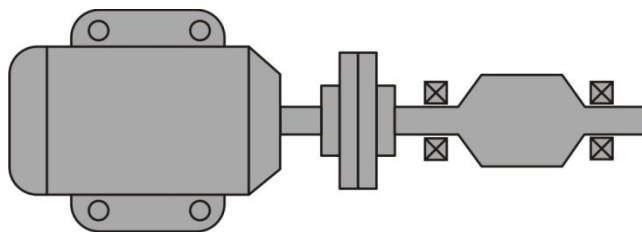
Схема контроля механических потерь в подшипниках быстроходного вала-червяка
